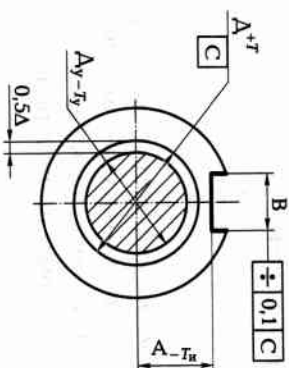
Схема установки заготовки цилиндрическим отверстием на цилиндрический установочный элемент приспособления при обработке паза
